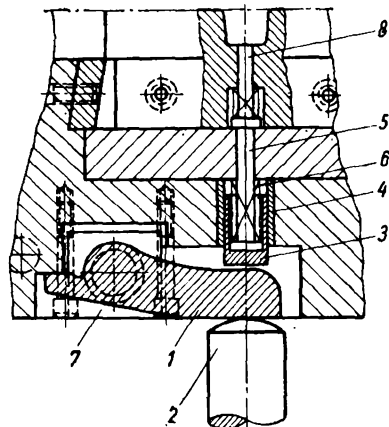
Рычажно-кулачковый выталкивающий механизм: 1 — рычаги; 2 — стержень выталкивания пресса; 3 — стакан; 4 — направляющая втулка; 5 — стержень; 6 — пружина; 7 — подшипники разъемные; 8 — толкатель
